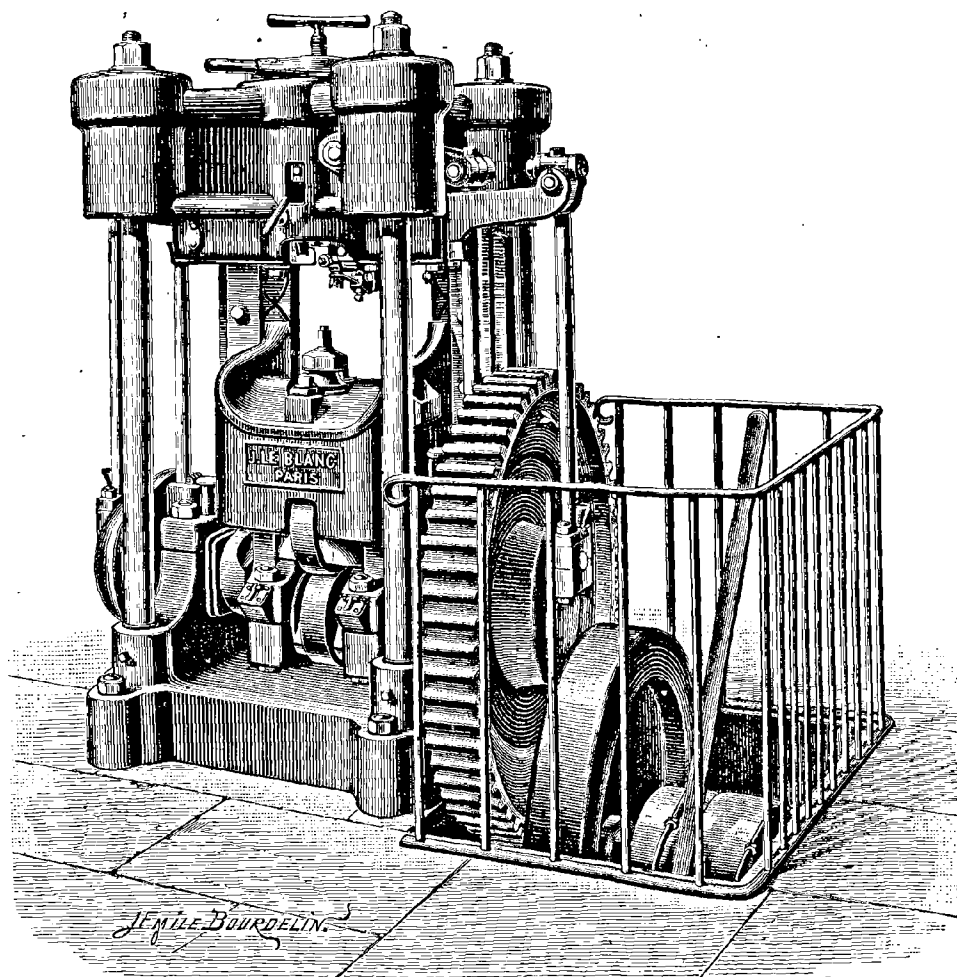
Machine à forger les écrous de M. Le Blanc.
